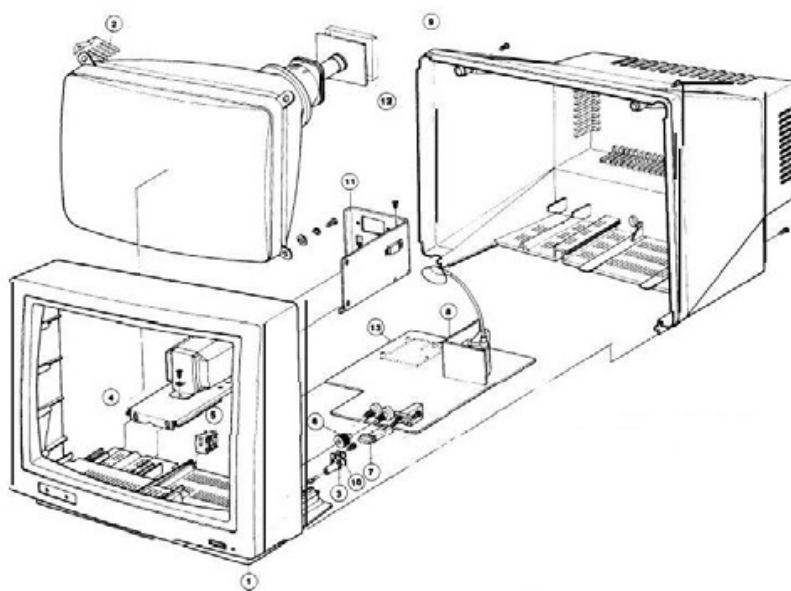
Despiece explosivo componentes de un televisor con TRC.
